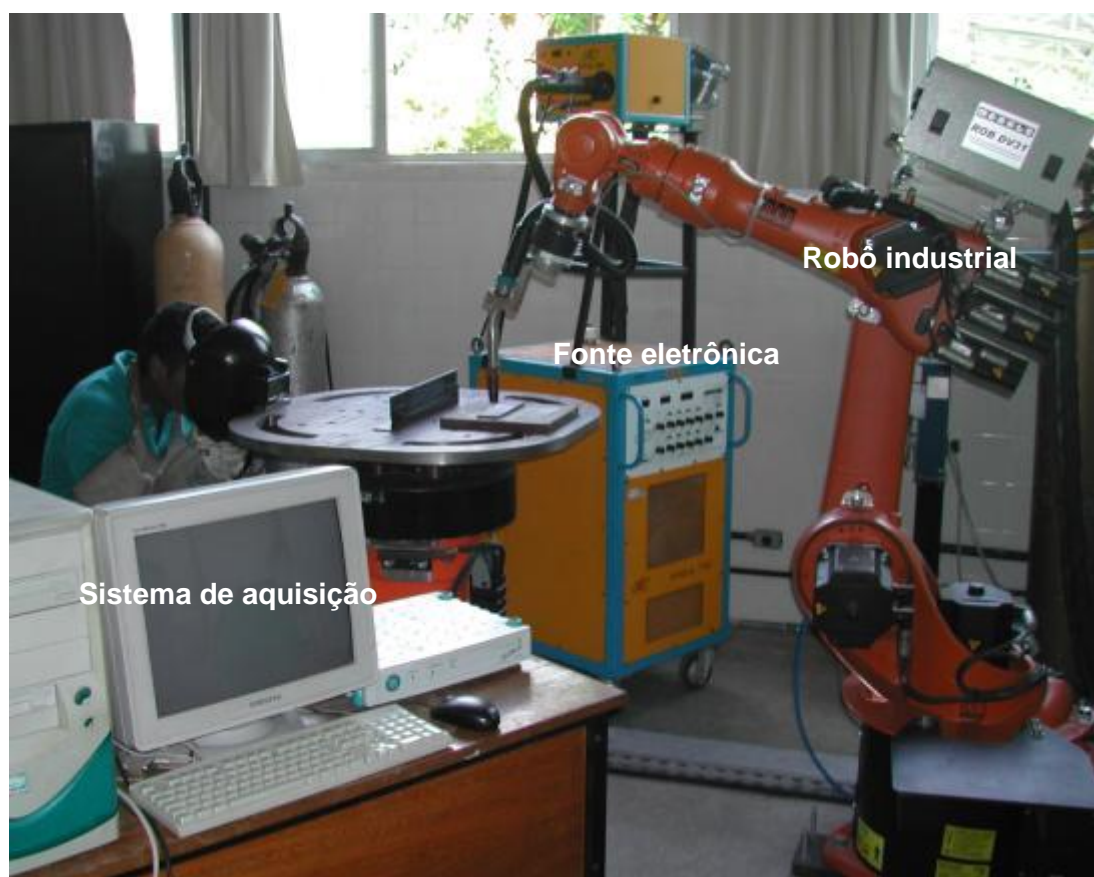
Equipamentos para soldagem: fonte eletrônica multiprocesso, robô industrial para deslocamento automático da tocha de soldagem, anteparo para monitoramento do comprimento do arco e sistema de aquisição de dados para receber os sinais da fonte.
